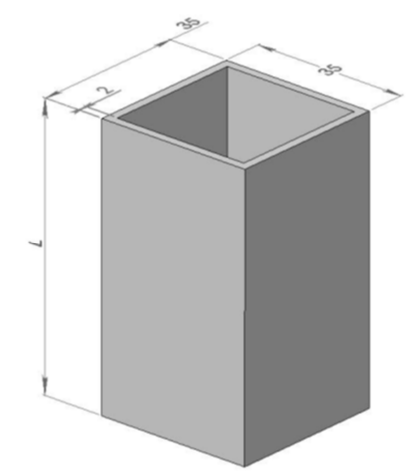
Les dimensions de structure tubulaire en aluminium à section carrée.
